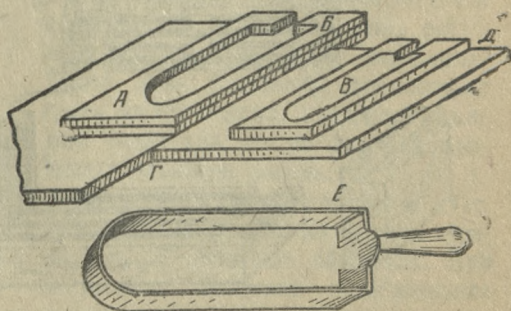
Форма и рамка для ручной формовки плоской черепицы
